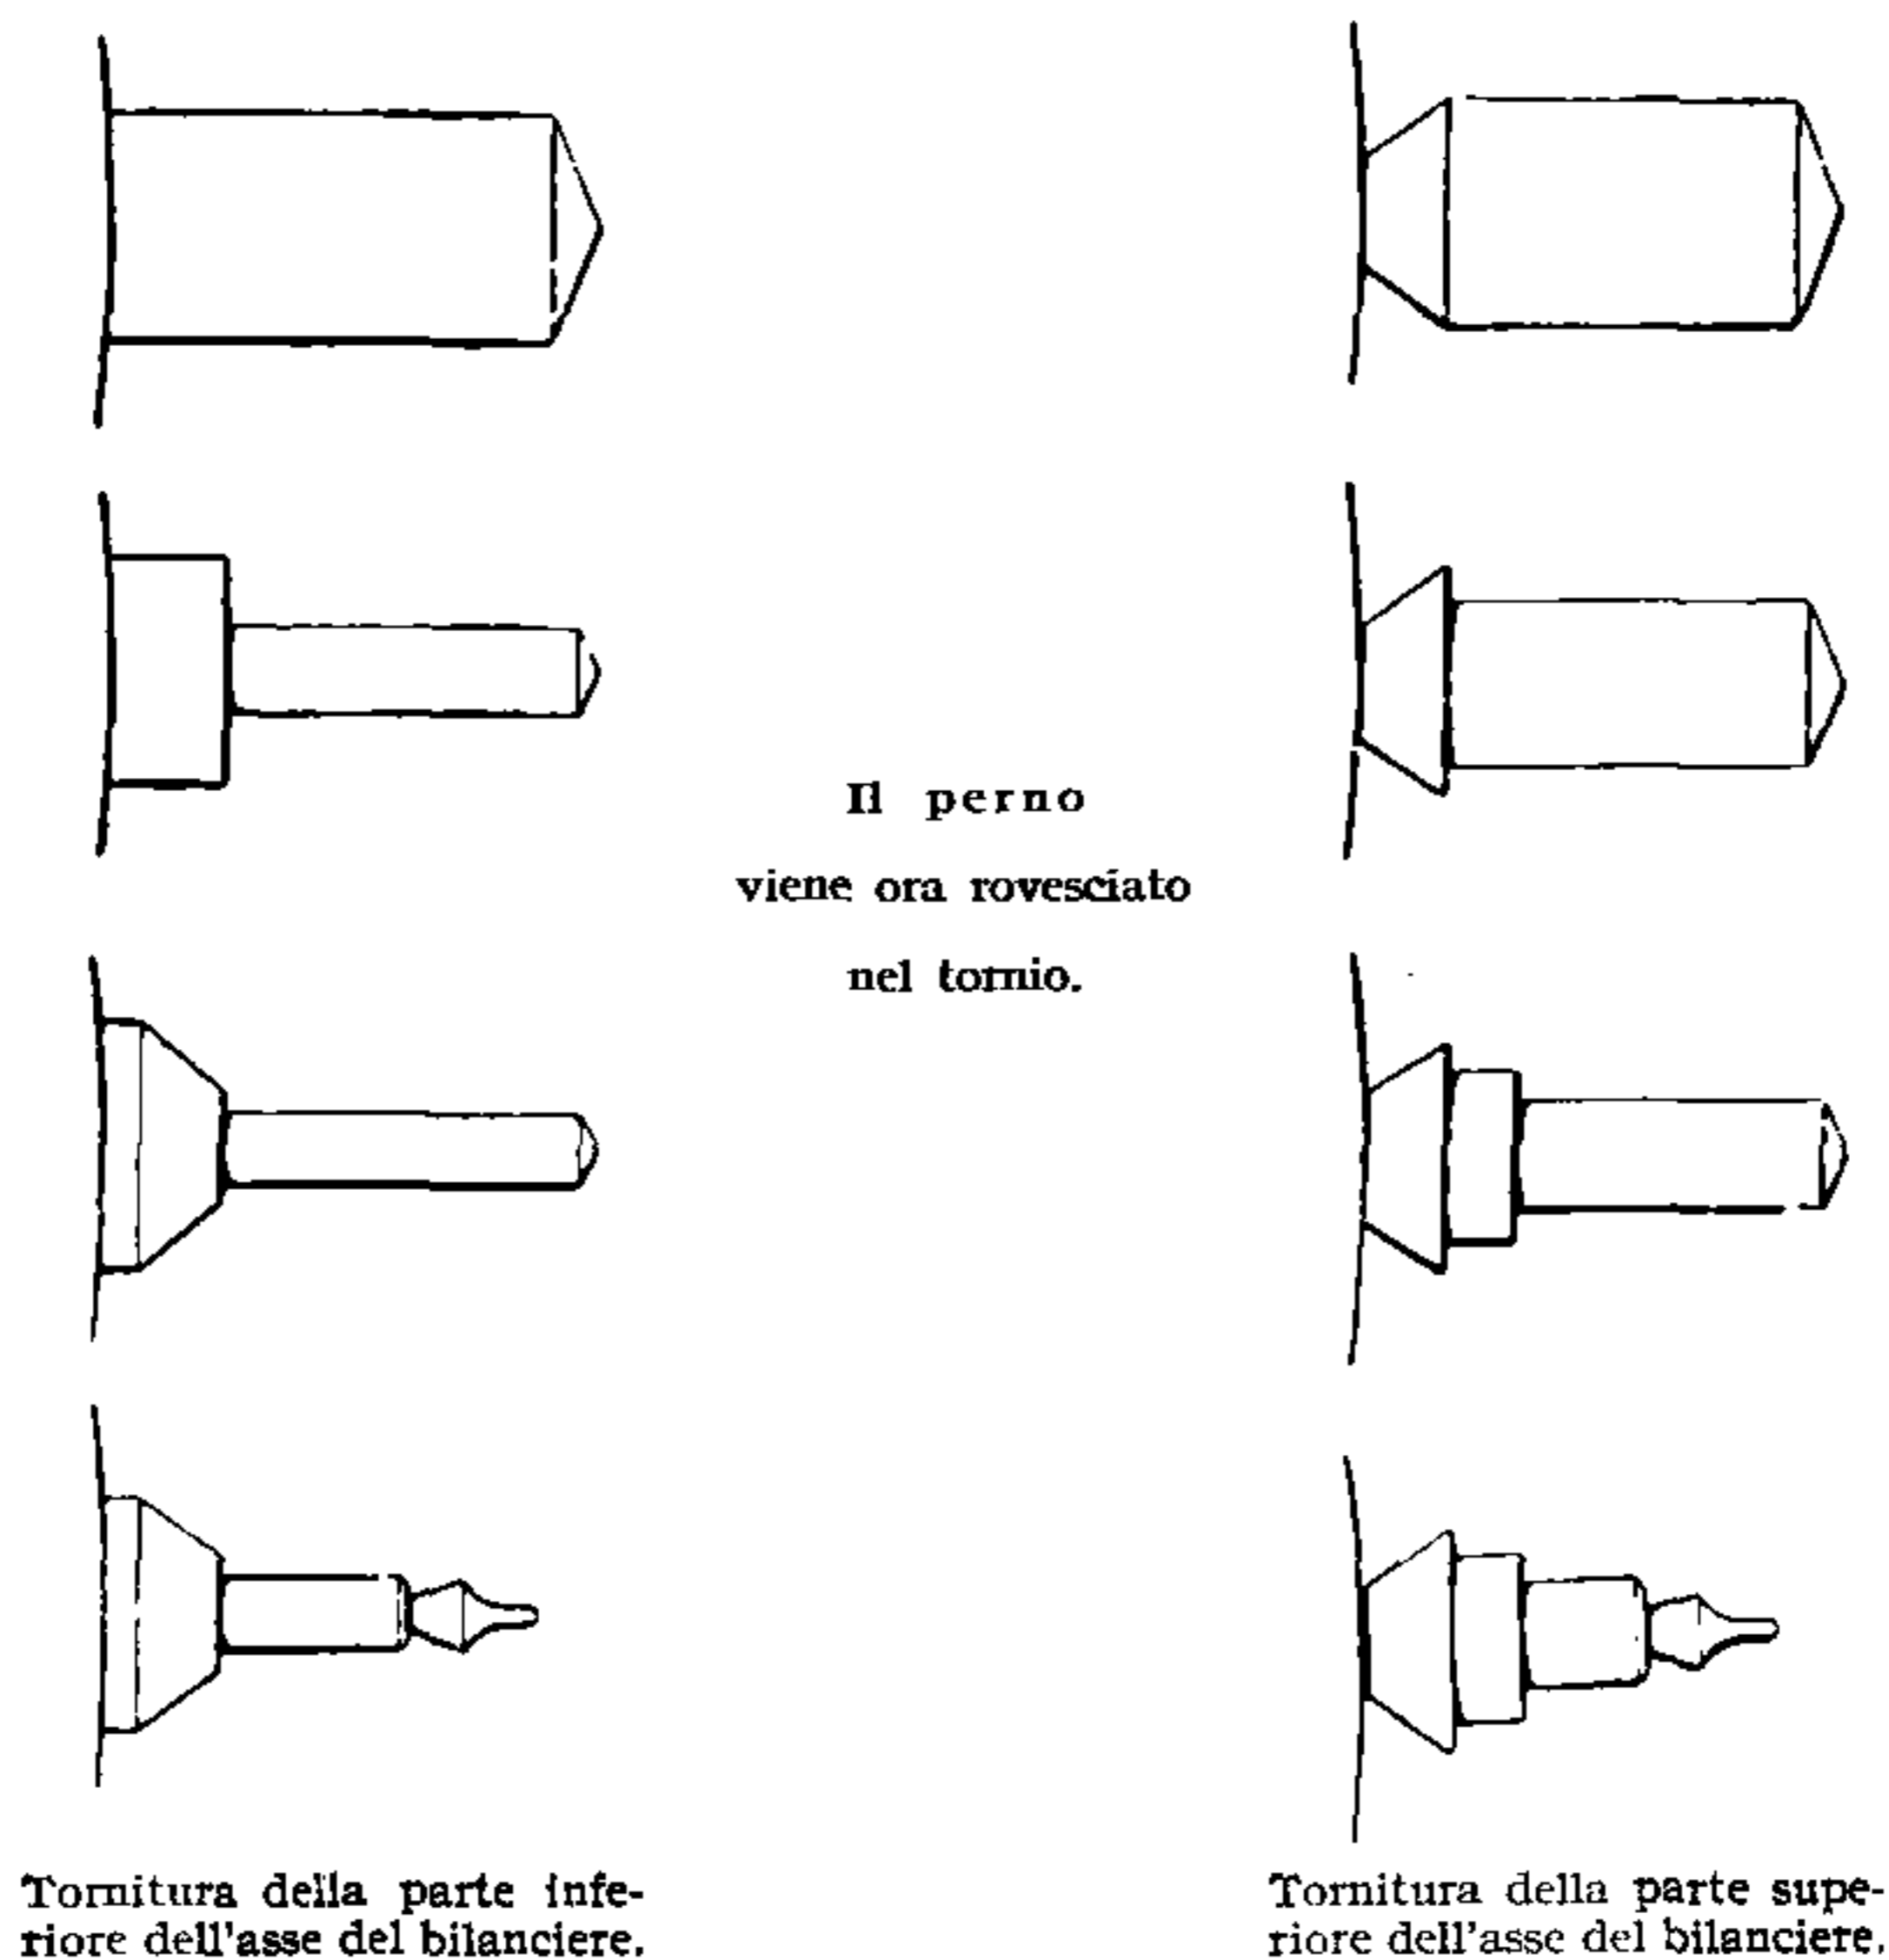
Otto fasi successive della tornitura di un asse del bilanciere.
